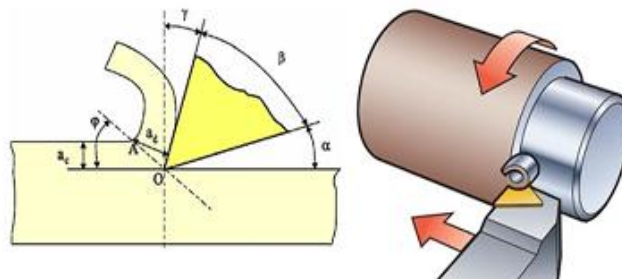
Manufactura por corte o arranque de viruta. [6]
